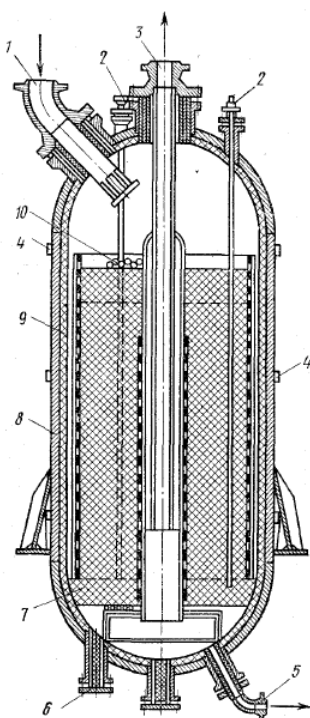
Реактор с аксиальным движением газо – сырьевой смеси [27]:
